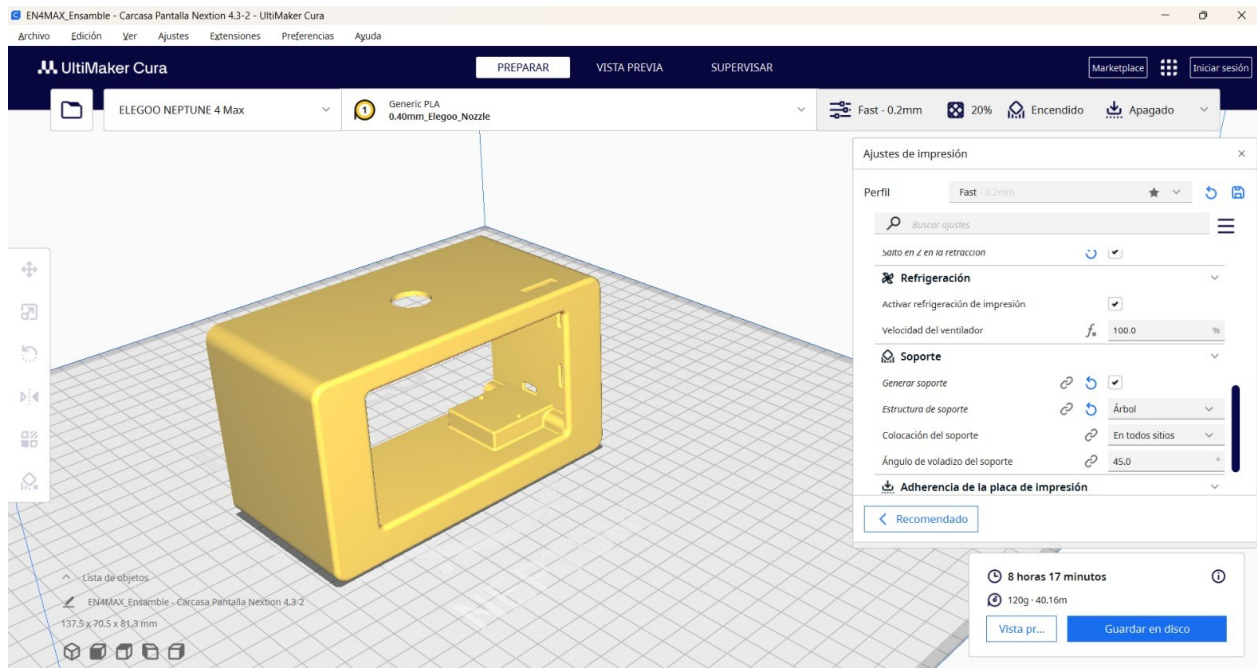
Entorno de ajustes de impresión 3D de la carcasa del robot.
